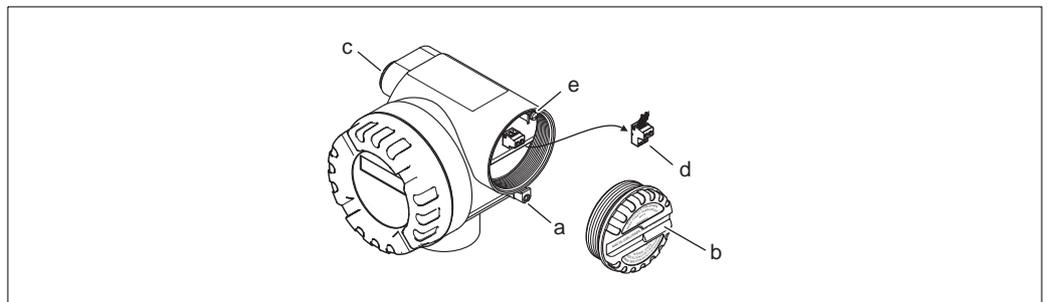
Anschluss des Messumformers Ex d Ausführung
